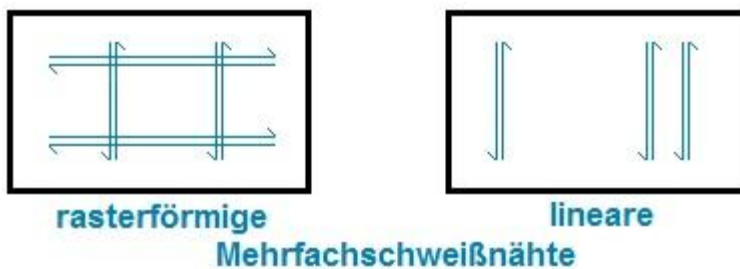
Skizze der Mehrfachschweißnähte
